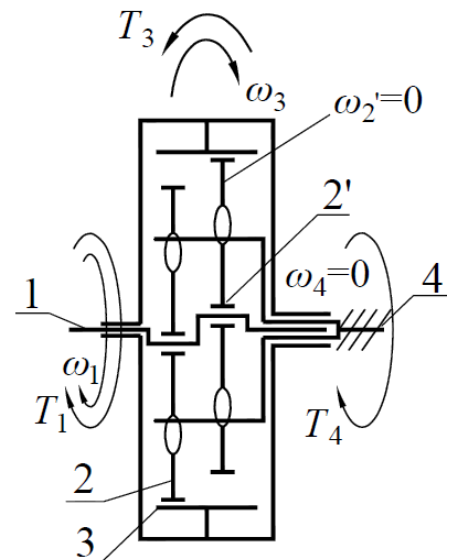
Схема кривошипно-планетарного редуктора для лебідок
